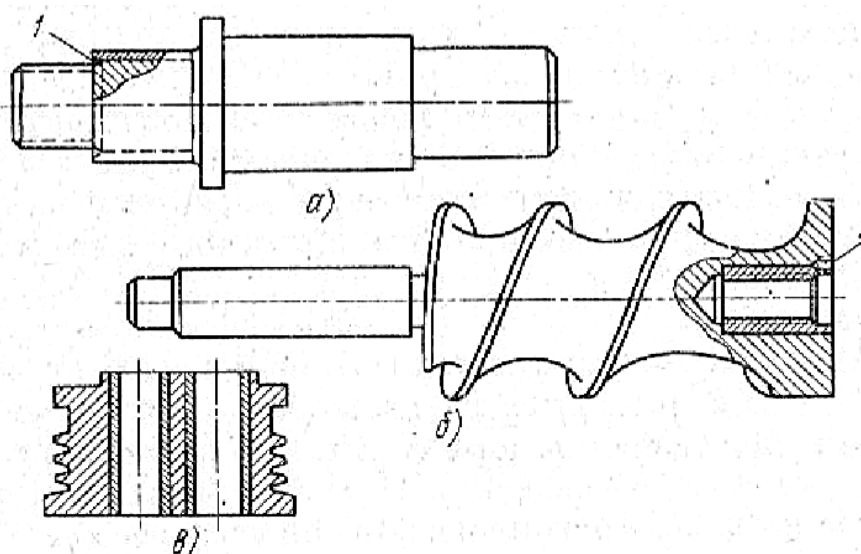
Установка добавочных ремонтных втулок на шейке вала (а), на шнеке мясорубки (б) и в блоке цилиндров (в):
